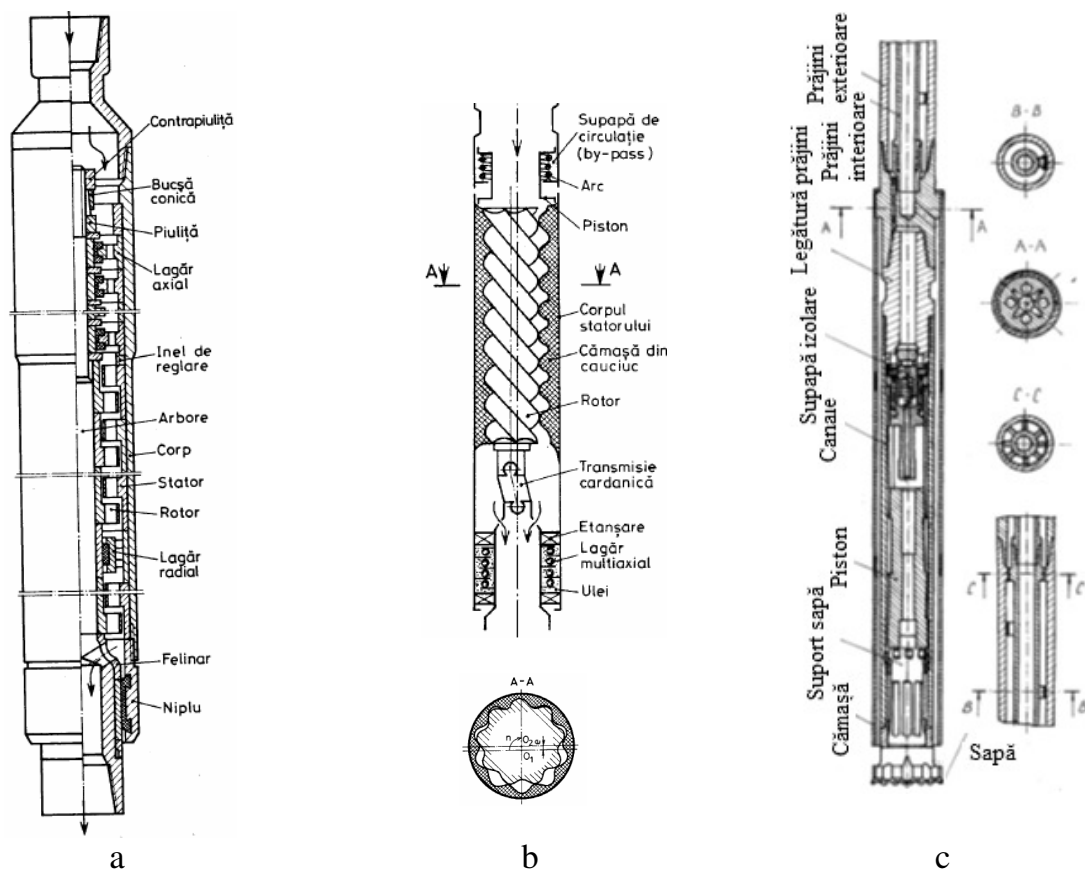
Motoare de adâncime folosite în foraj: a) turbina de foraj; b) motorul elicoidal; c) motorul roto-percutant.
